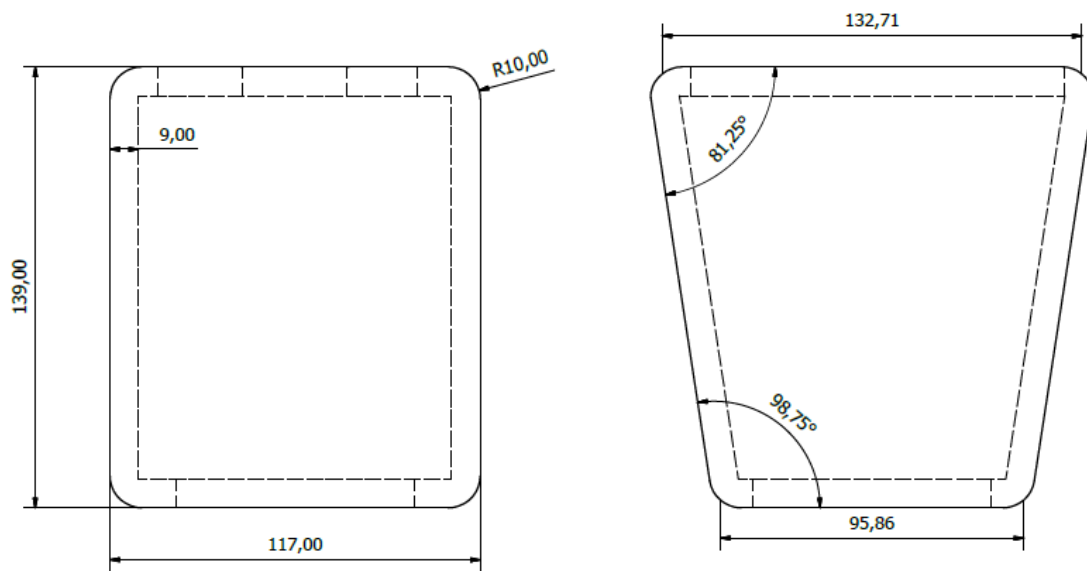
Dimensiones de la caja de aspiración en su vista frontal y lateral.
